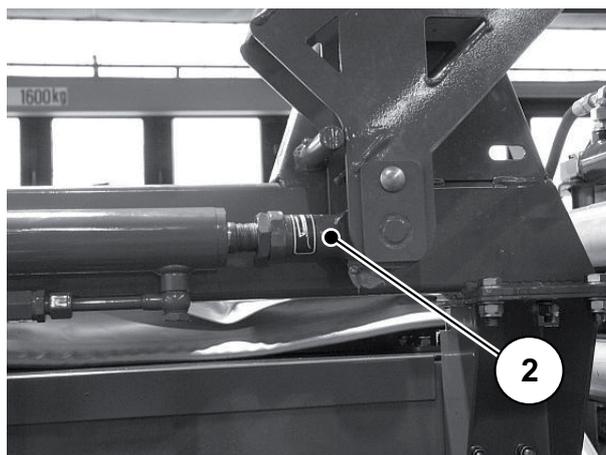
Гидроцилиндр для фиксатора штанги
